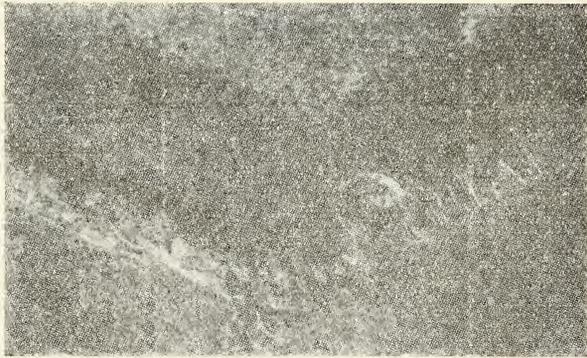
Aspecto correcto de una soldadura de unión en una pieza estructural compuesta por chapas de acero.
